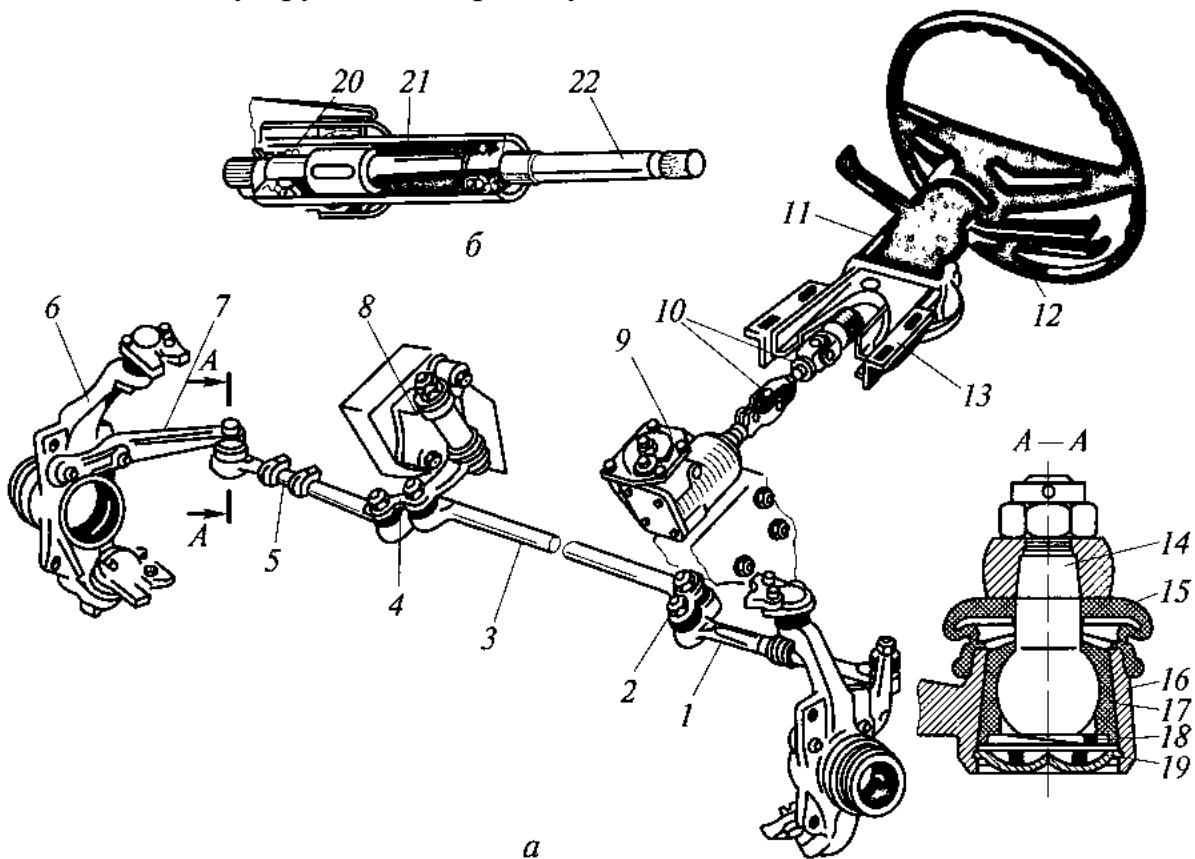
Рульове керування легкових автомобілів ВАЗ підвищеної прохідності: *а* - загальний вигляд; *б* - установка рульового вала; 1, 3 - тяги; 2 - сошка; 4, 7 - важелі; 5 - муфта; 6 - кулак; 8, 13 - кронштейни; 9 - картер; 10 - вали; 11 - колонка; 12 - рульове колесо; 14 - палець; 15 - чохол; 16 - кінцевик; 17 - вкладиш; 18 - пружина; 19 - заглушка; 20 - підшипник; 21 - труба; 22 - рульовий вал.
